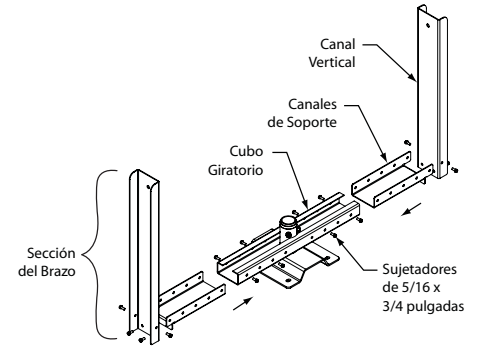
Conjunto de Soporte de Montaje en Cielo
